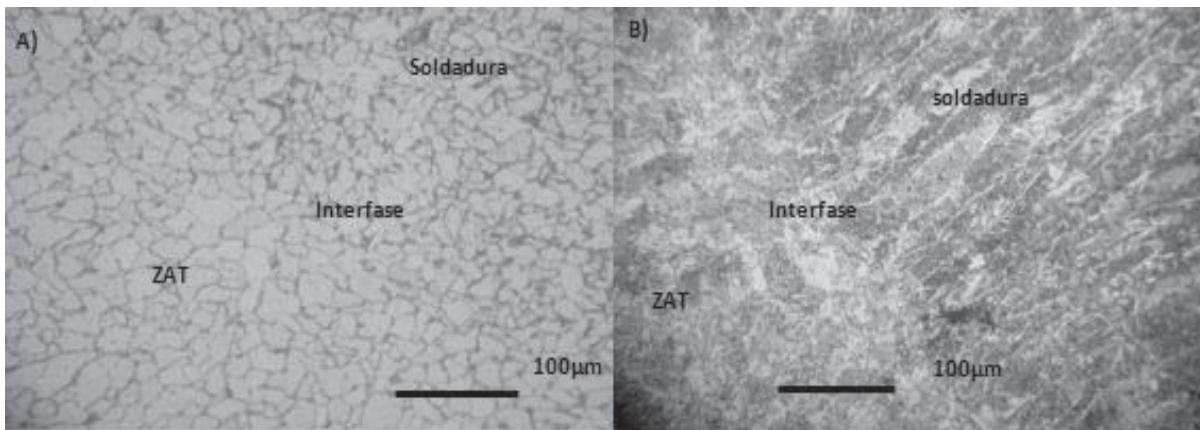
Interface de los cordones de soldadura a) con electrodo húmedo y b) electrodo seco [3]
